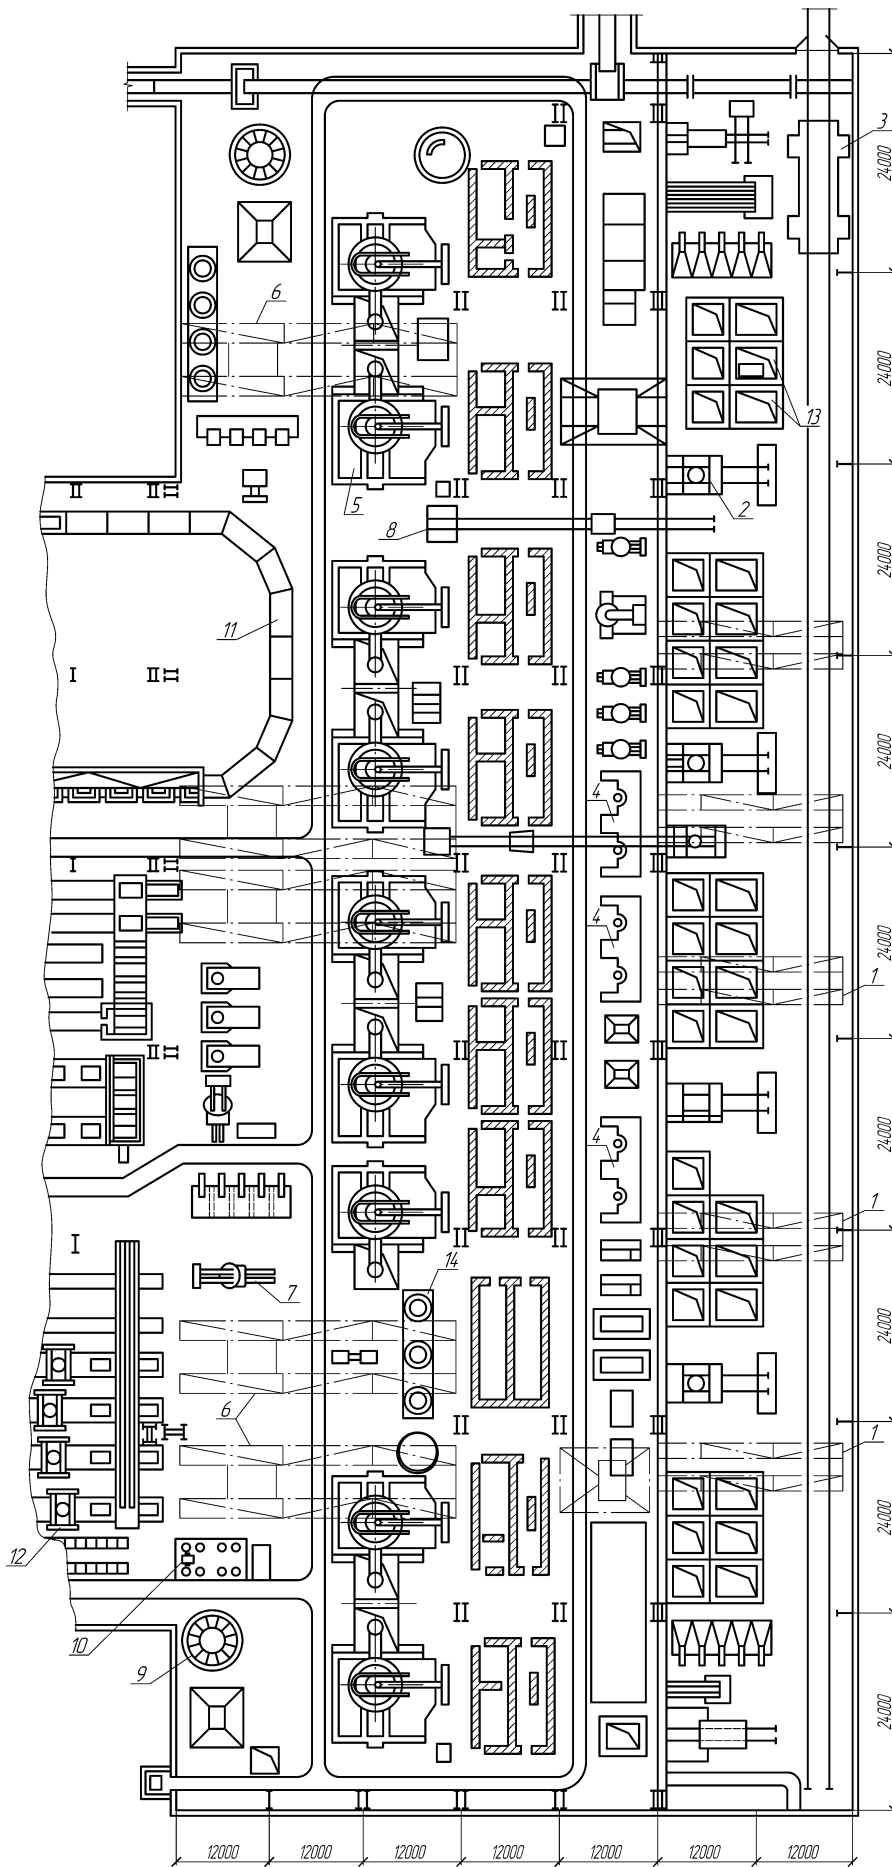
Планировка цеха тяжелых стальных отливок с электрическими дугowymi печами: 1 - кран мостовой 30/5т; 2 - тележка для транспортировки бады с шихтой; 3 - весы платформенные; 4 - стенд для выбивки и ремонта ковшей; 5 - электропечь дуговая сталеплавильная 25 т; 6 - кран мостовой 50/10 т; 7 - стенды для подогрева ковшей; 8 - люк для подачи бады с металлическим ломом; 9 - место для набора сводов электропечей; 10 - сушило для стопоров; 11 - линия охлаждения литейного конвейера; 12 - передвижные стенды с ковшами для заливки форм;
